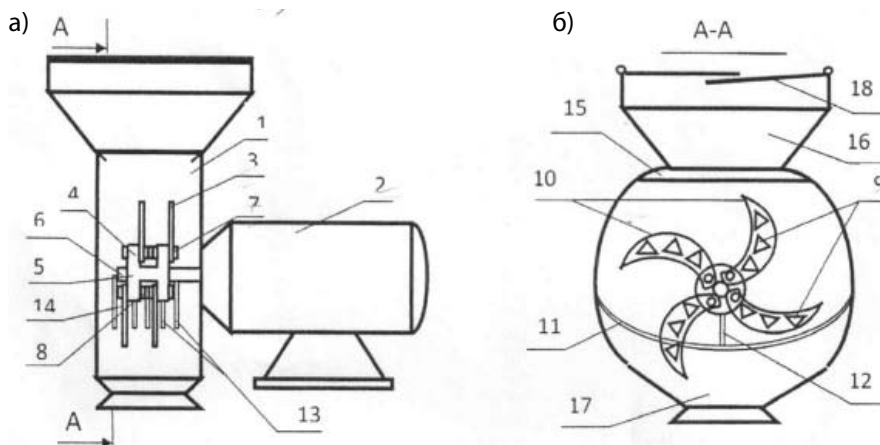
Опытный измельчитель корнеклубнеплодов
